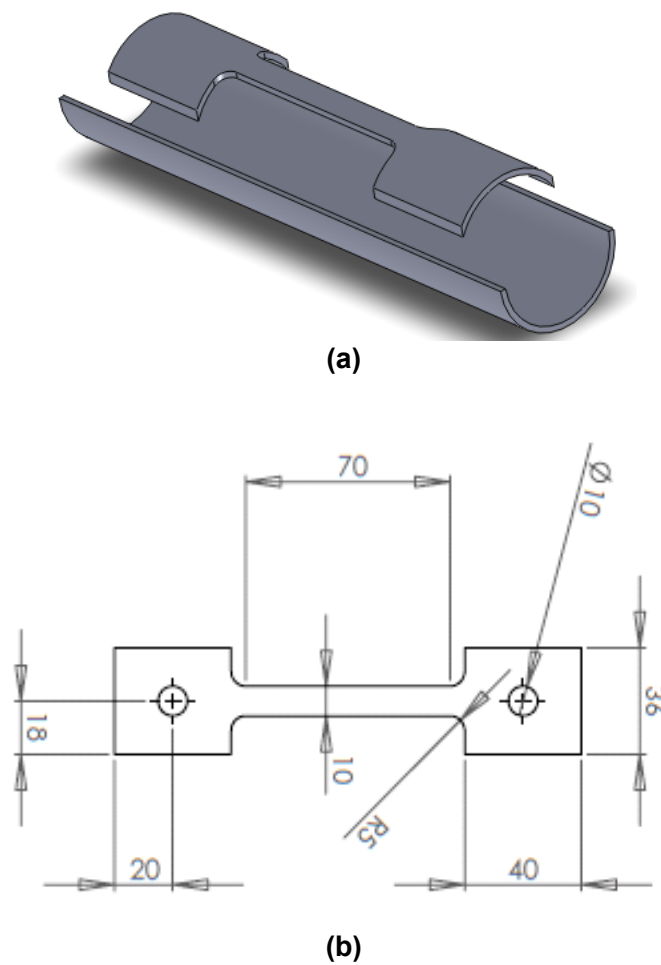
(a) Desenho do corpo de prova retirado do tubo de aço 2,25Cr-1Mo; (b) vista superior apresentando suas dimensões.
